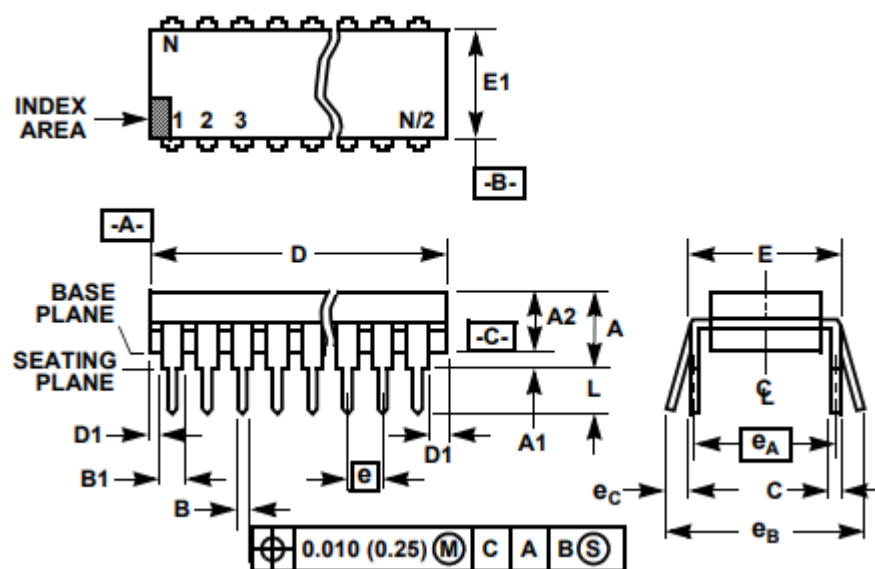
Габаритный чертеж драйвера ISL83202IBZT
